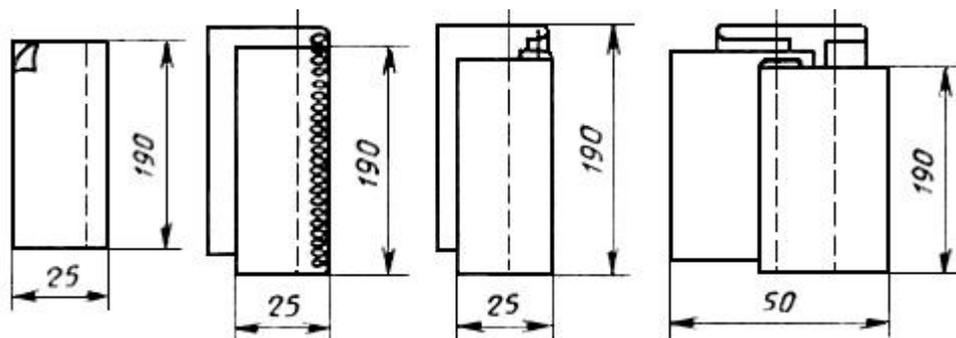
Схема изготовления проб для испытаний при приложении растягивающей нагрузки вдоль шва.
